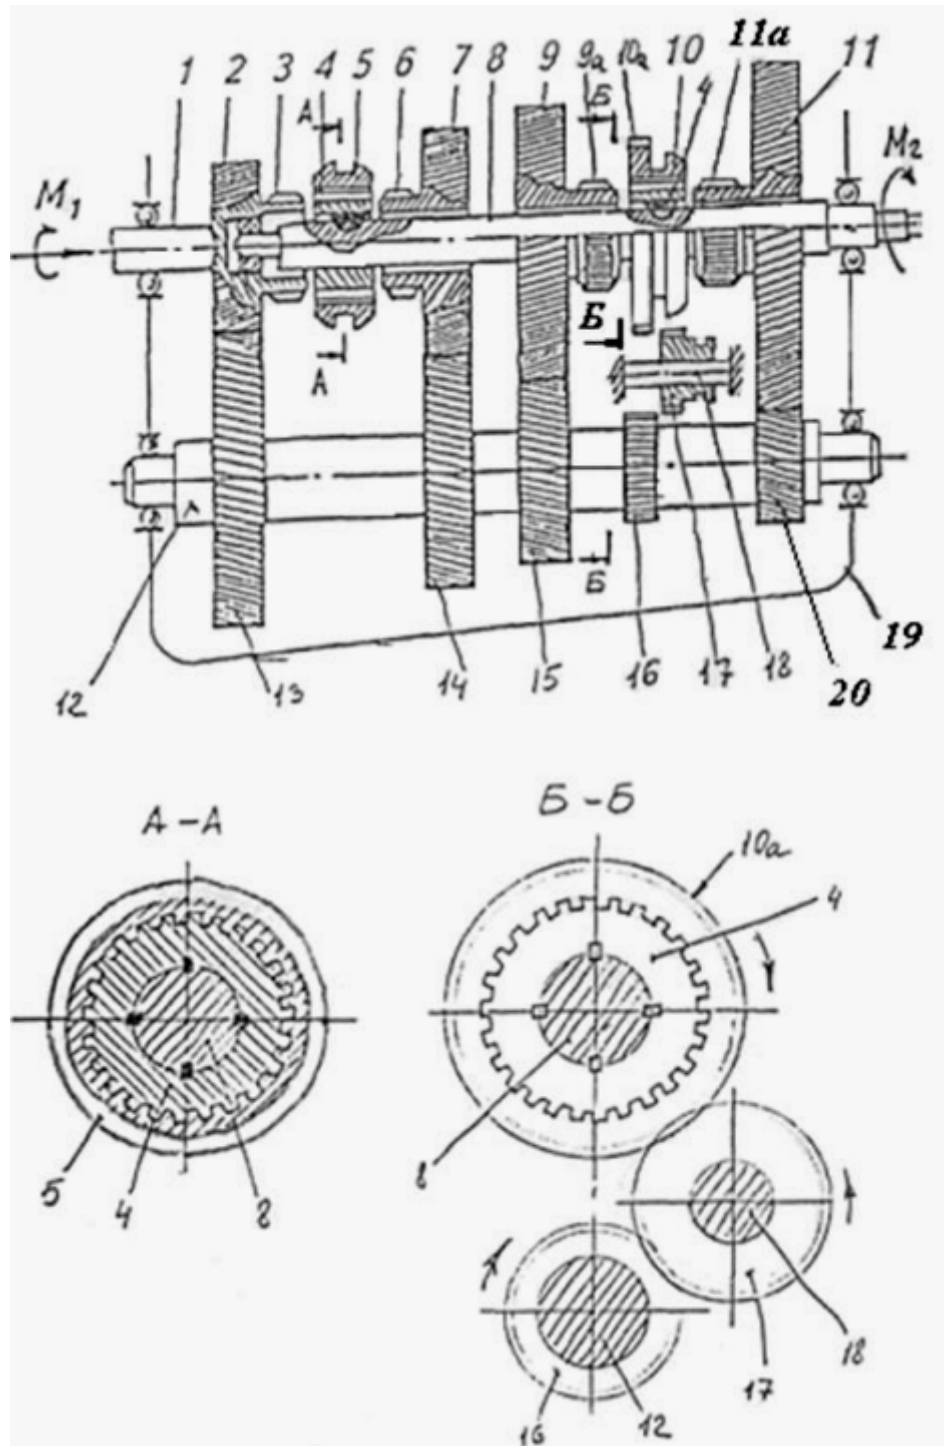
Схема трехвальной четырехступенчатой коробки передач: 1, 8 и 12 - соответственно первичный вторичный и промежуточный валы; 2 - зубчатое колесо постоянного зацепления первичного вала; 3, 6 - зубчатые венцы; 4 - зубчатая ступица; 5, 10 - скользящие зубчатые муфты; 7, 9 и 11 - зубчатые колеса постоянного зацепления вторичного вала;
